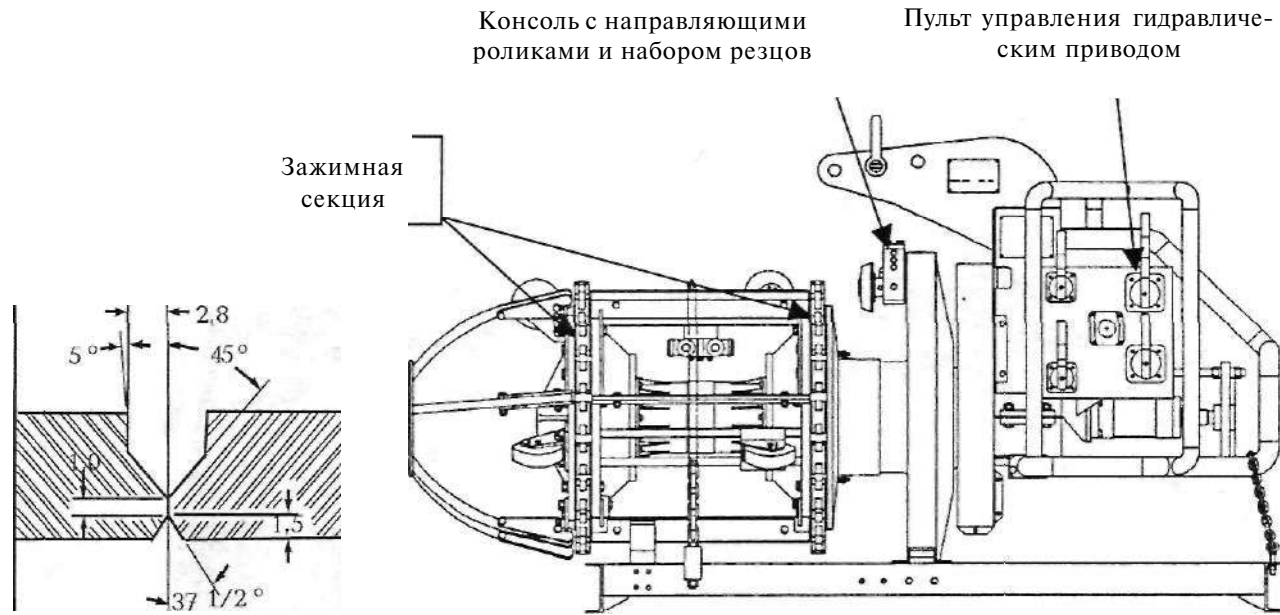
Станок для обработки кромок труб (схема) и форма разделки кромок
